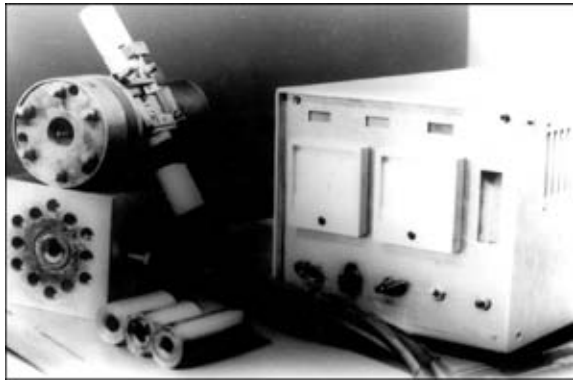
Сварочный автомат «Комета-М» для сварки труб с трубными решетками погруженной дугой
